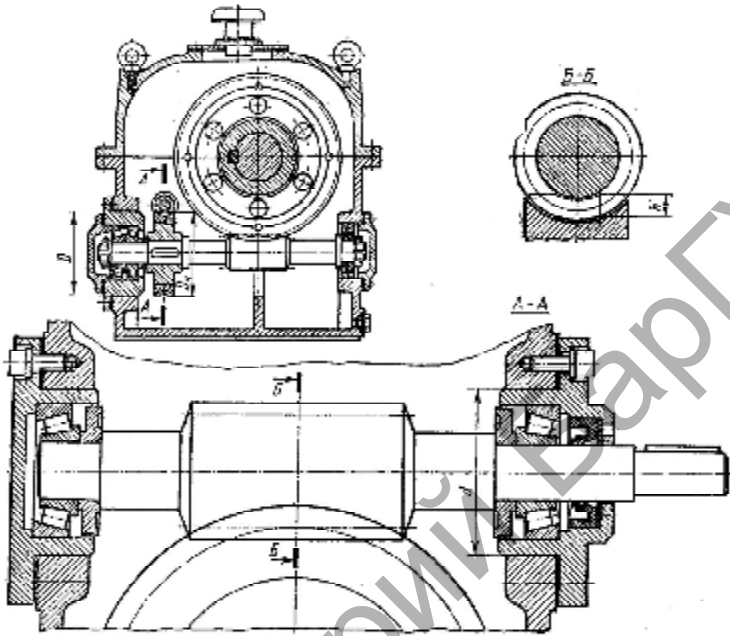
Предварительная раздвижка осей при сборке червячного редуктора [18]
